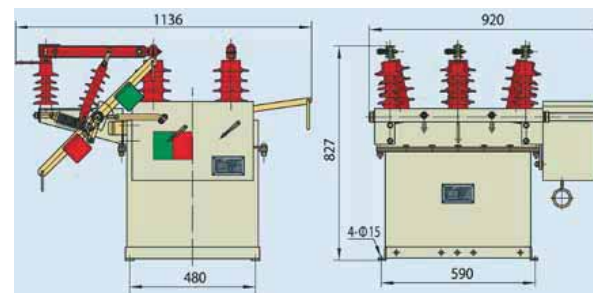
Выключатель ZW8-12 с разъединителем
